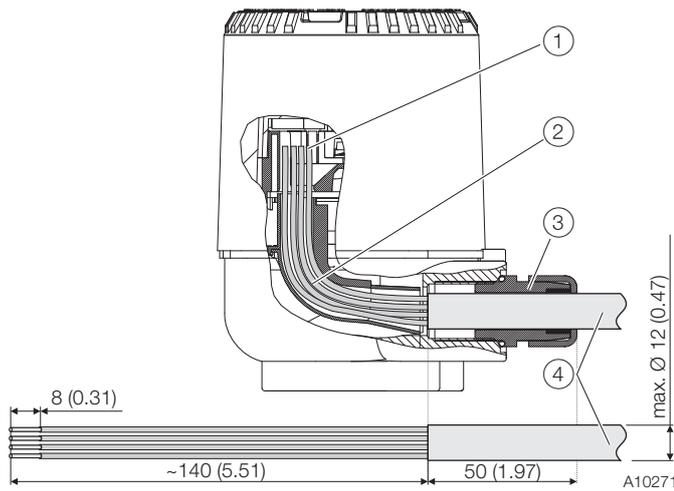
Anschluss am Messumformer, Abmessungen in mm (inch)
